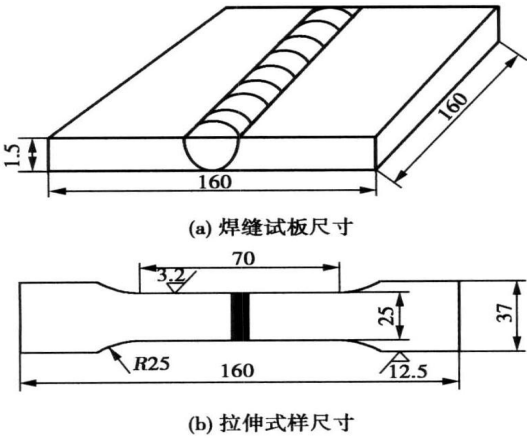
焊接试板及拉伸试样尺寸 (mm)
